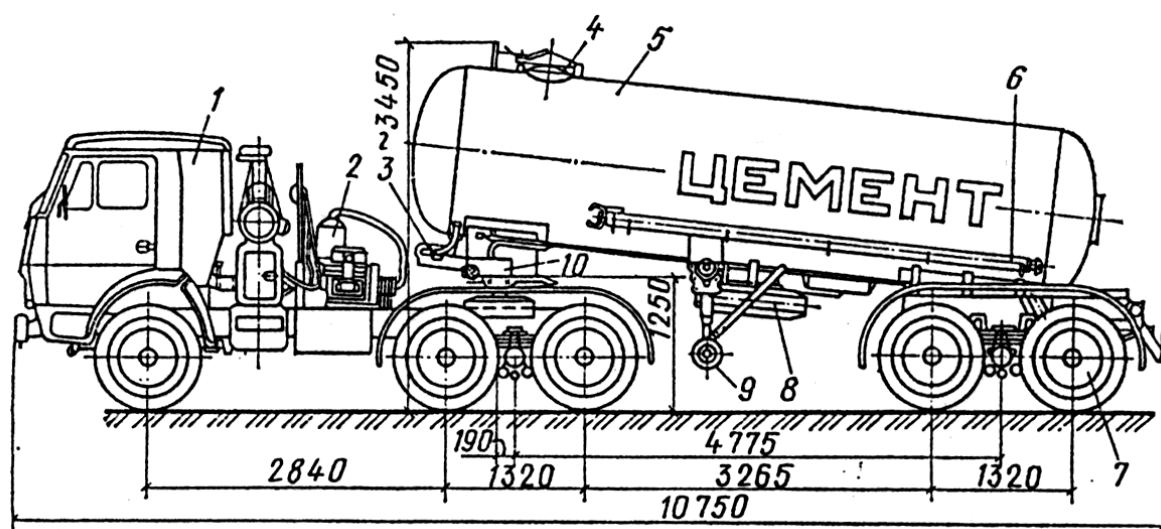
Автоцементовоз с пневморазгрузкой ТЦ – 11: 1 – седельный тягач КамАЗ-5410; 2 – компрессорная установка; 3 – пневмооборудование для разгрузки; 4 – загрузочный люк; 5 – цистерна-полуприцеп; 6 – разгрузочный рукав; 7 – ходовая часть; 8 – запасное колесо; 9 – опорное устройство; 10 – сцепное устройство
